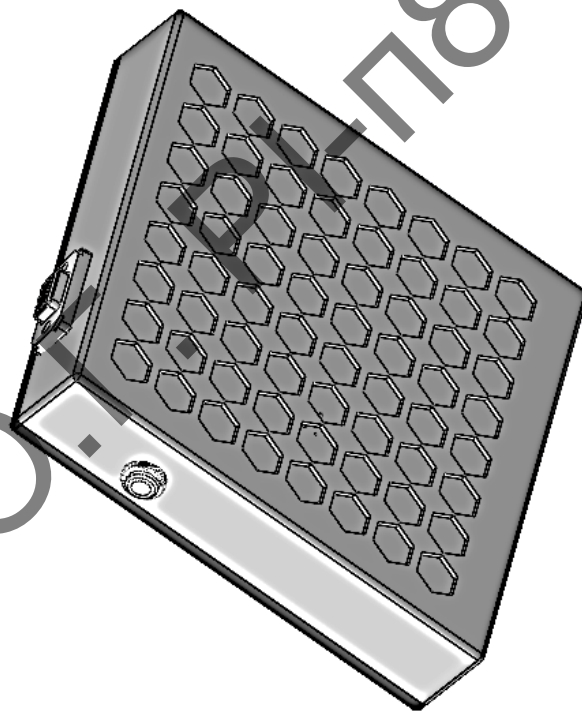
Зовнішній вигляд корпусу пристрою
